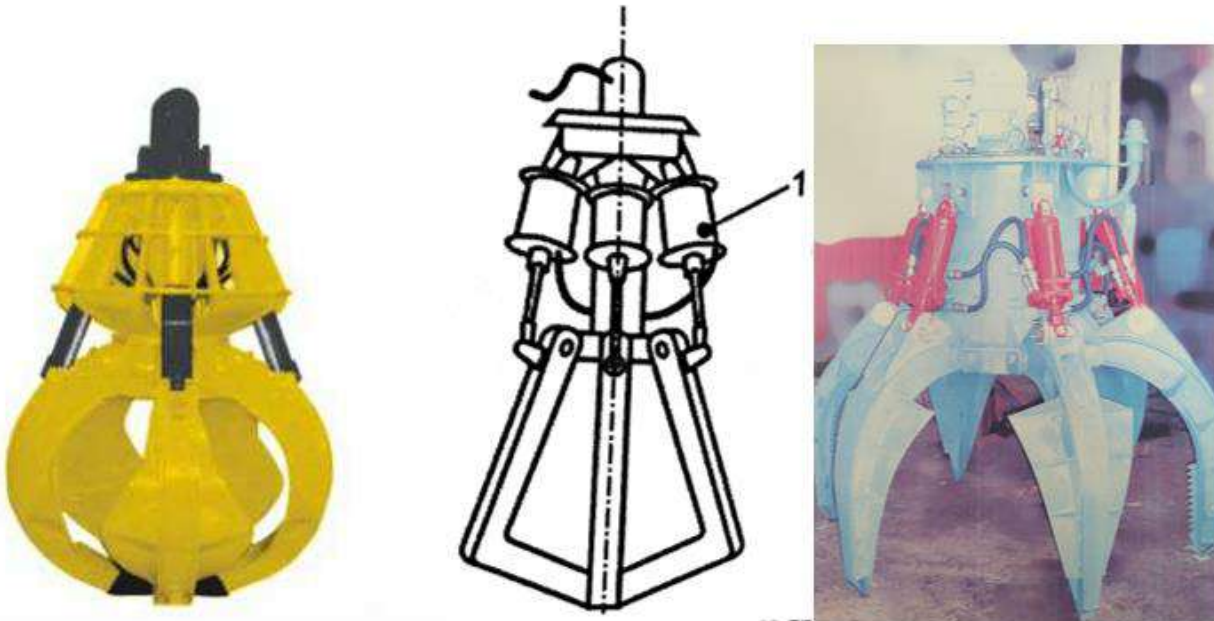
Схема і загальний вигляд багатощелепного грейфера з індивідуальними гідро-приводами кожної щелепи
